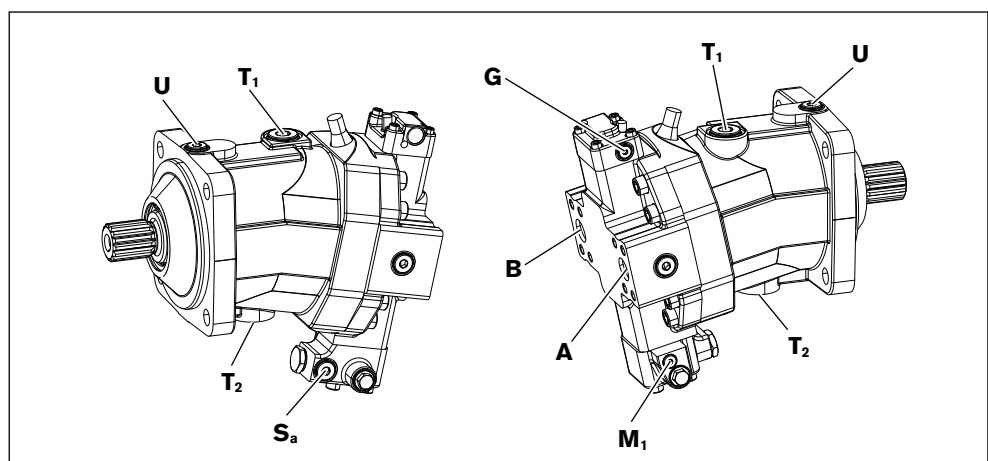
Vue d'ensemble des raccords A6VM avec réglage HP5/HP6 et valve de rinçage, raccords de service sur le côté
